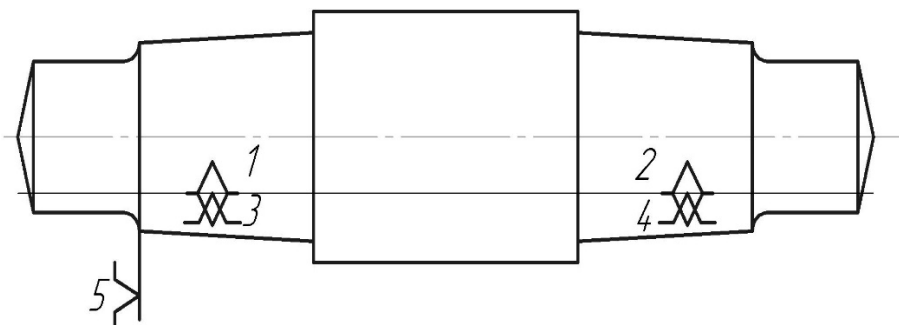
Теоретична схема базування заготовки валу для першої операції
